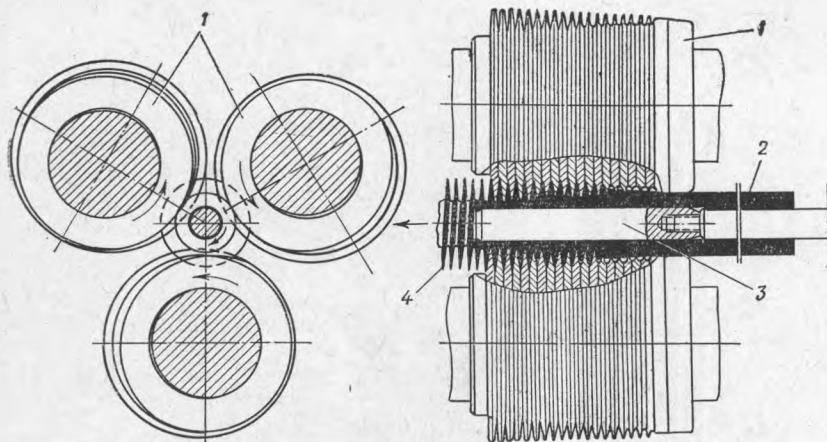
Схема прокатки ребристых труб в кольцевых калибрах:
